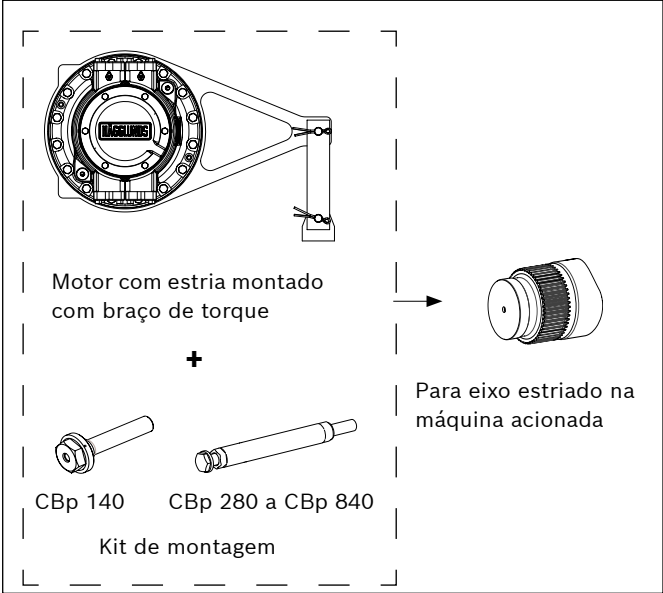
Montagem do braço de torque de uma terminação para eixo estriado
